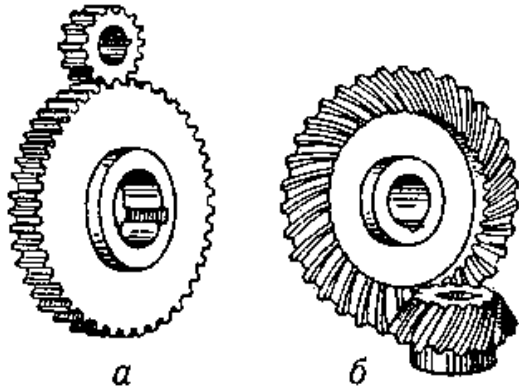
Передачи: а – зубчатая цилиндрическая; б – зубчатая коническая
